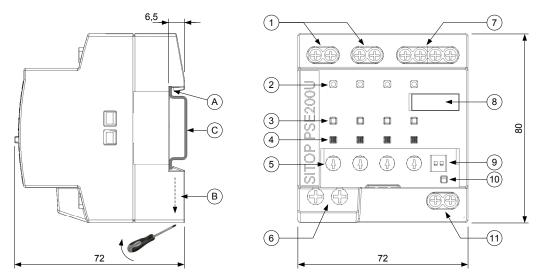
Maßbild (mm) Figure 1: Dimension drawing (mm)
